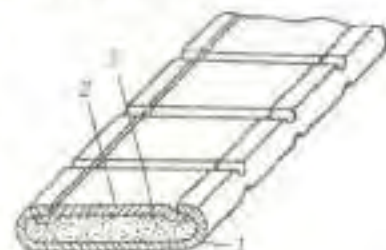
Порошкова стрічка: 1 — ядро стрічки; 2 — верхня стрічка; 3 — шпакелі
